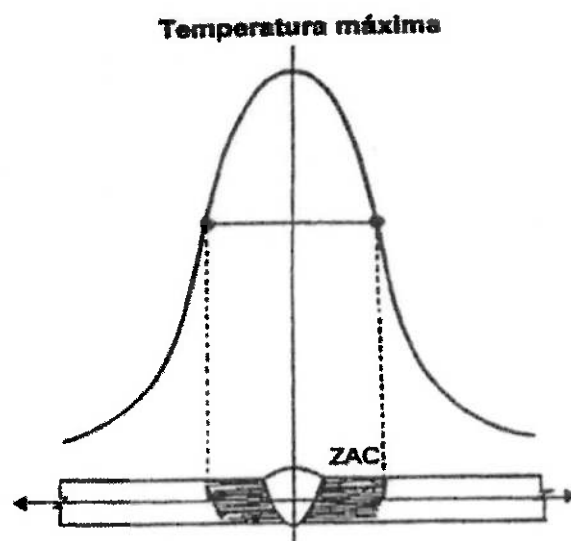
Repartição térmica de uma junta soldada ⁽¹⁴⁾.
